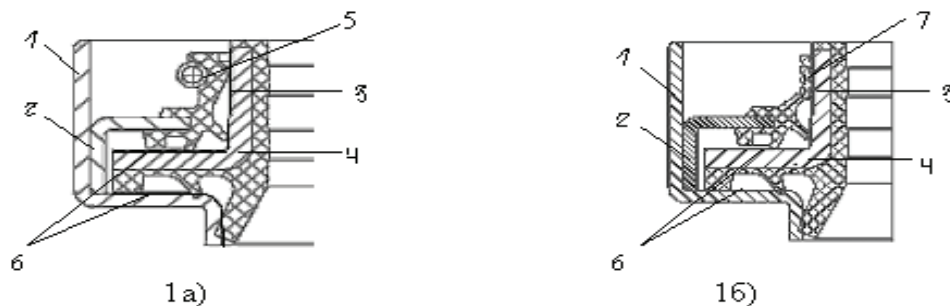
Конструкция кассетного сальника дискатора БДМ 60x85x15, а — классическая «губа», б — коническая «губа»: 1 — каркас металлический наружный уплотняющий обоймы, 2 — каркас металлический втулки с рабочей частью, 3 — шлифованная поверхность гильзы, 4 — каркас металлический внутренней уплотняющей гильзы, обрезиненной на поверхности уплотнения вала, 5 — пружина, 6 — лакированные поверхности, 7 — коническая «губа»
